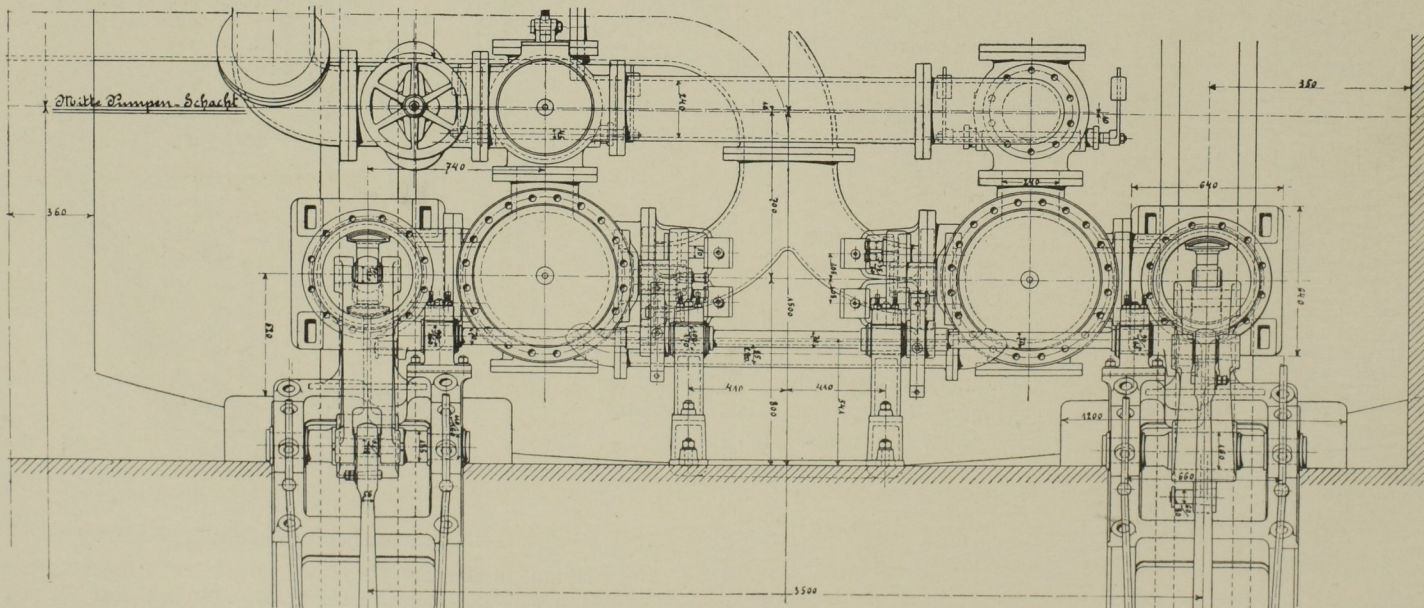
Grundriss der Druckpumpen. Masst. 1 : 30.
